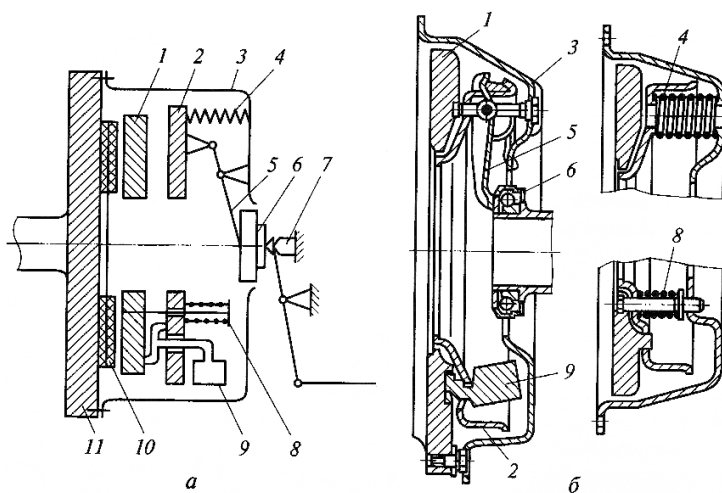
Схема (а) и конструкция (б) центробежного сцепления:
